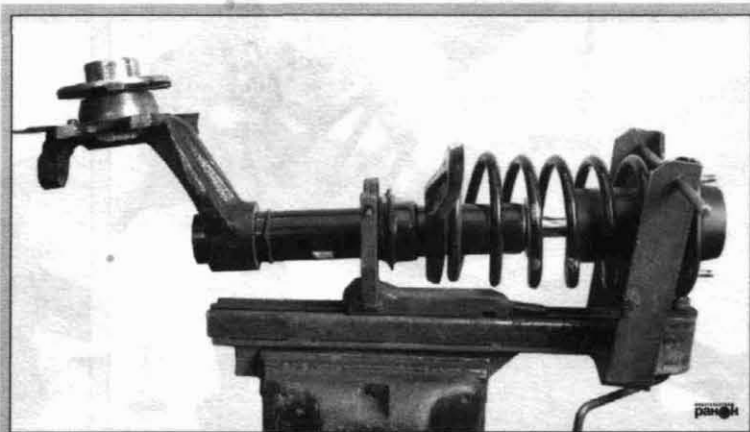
Стойка в приспособлении, подготовленная к разборке
